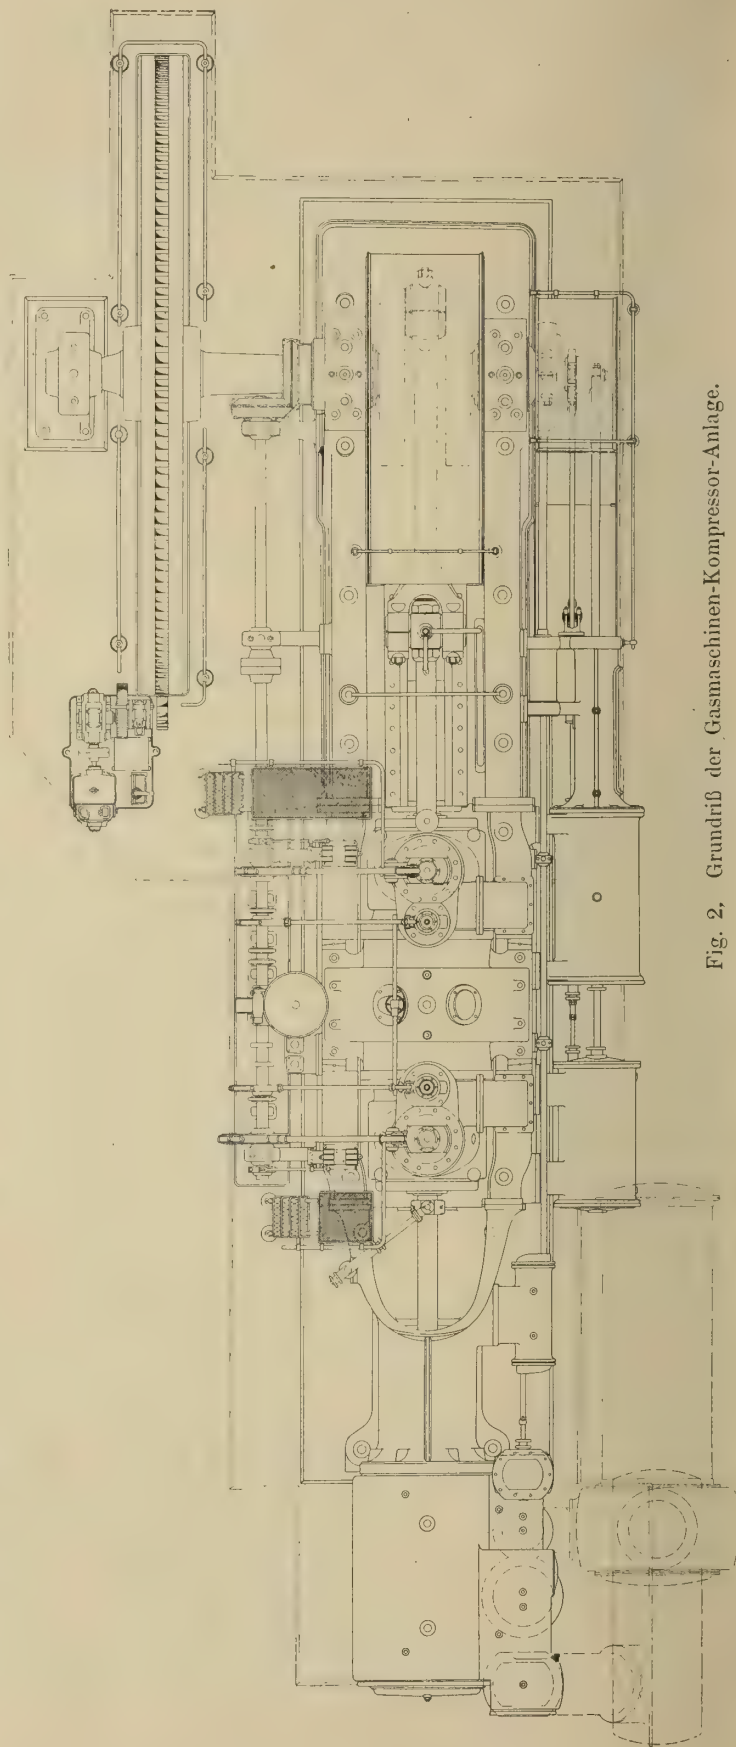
Grundriß der Gasmaschinen-Kompressor-Anlage.
